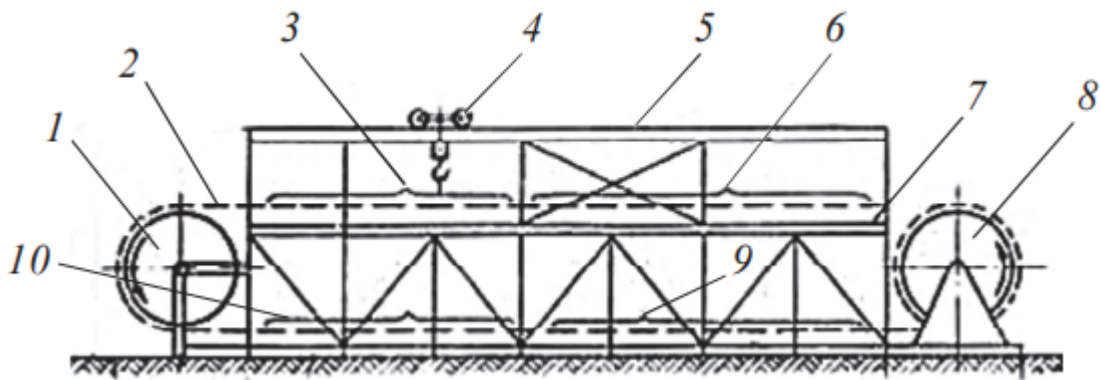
Установка для виготовлення полотен рулонних заготовок:
